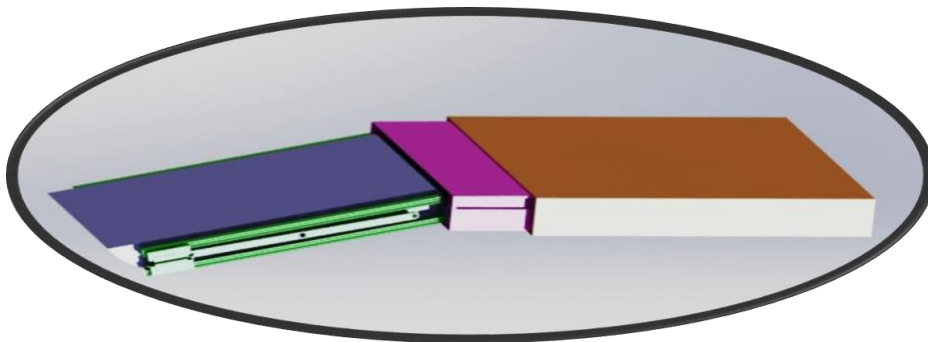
Vue latéral gauche de la plate –forme avec inclinaison de la
